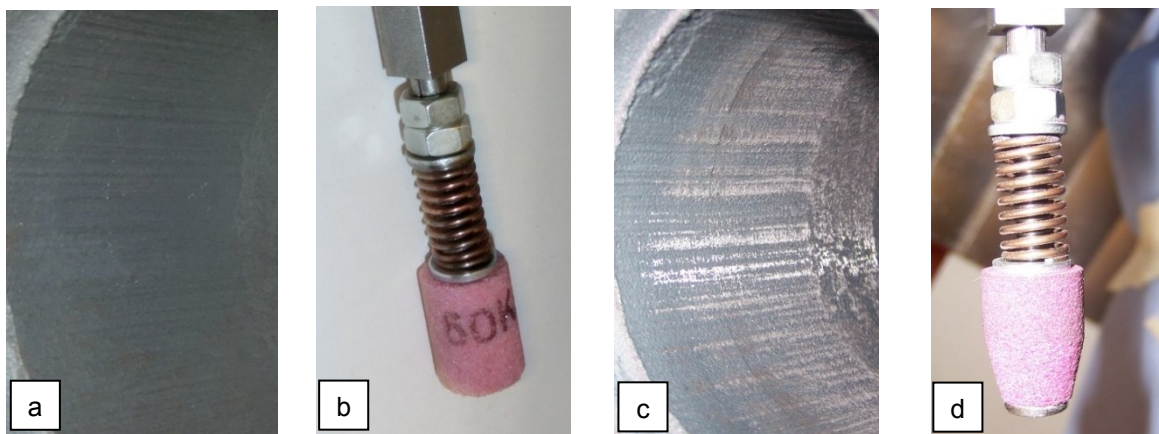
Versuchsträger vor der Bearbeitung (a) und nach der Bearbeitung mit dem Schleifstiftwerkzeug (c); Schleifstift vor dem Bearbeitungsversuch (b) und Verschleißzustand nach der Bearbeitung (d)
